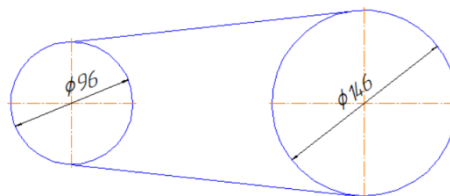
Кінематична схема привода дискового здрібнювача
